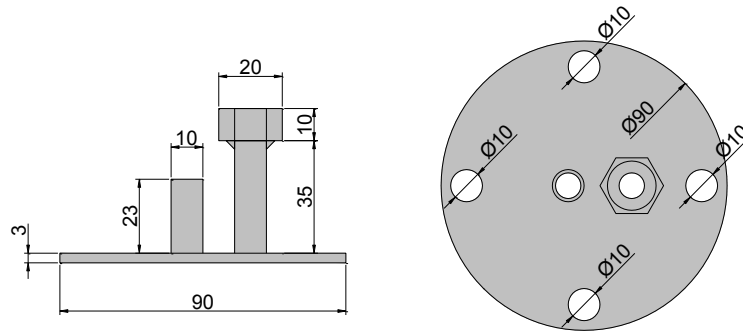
Cabeça da Autoclave, em perfil e planta, respetivamente
